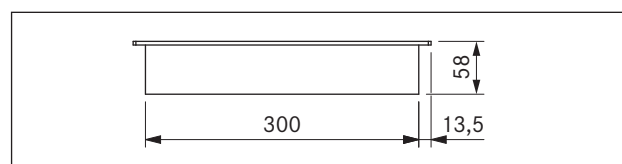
Dimensões do aparelho CKI, vista frontal
